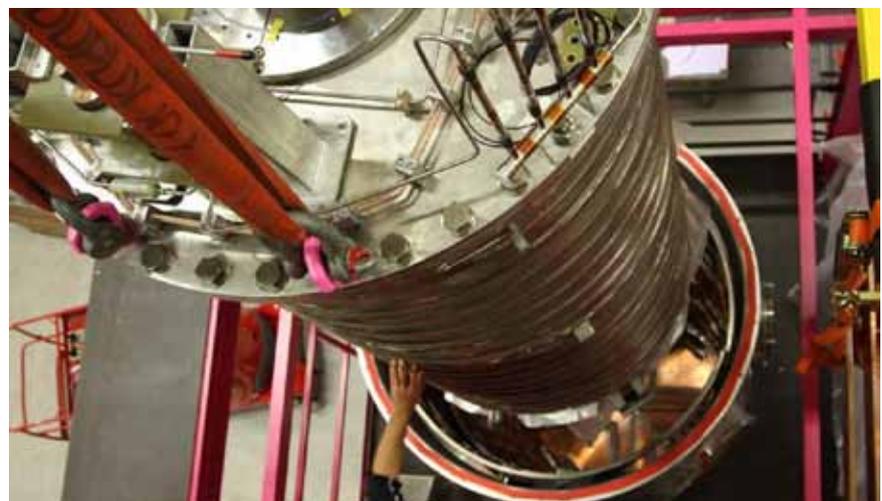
Insertion de l'assemblage des bobines de la nouvelle installation de test EDIPO dans la chambre à vide.
